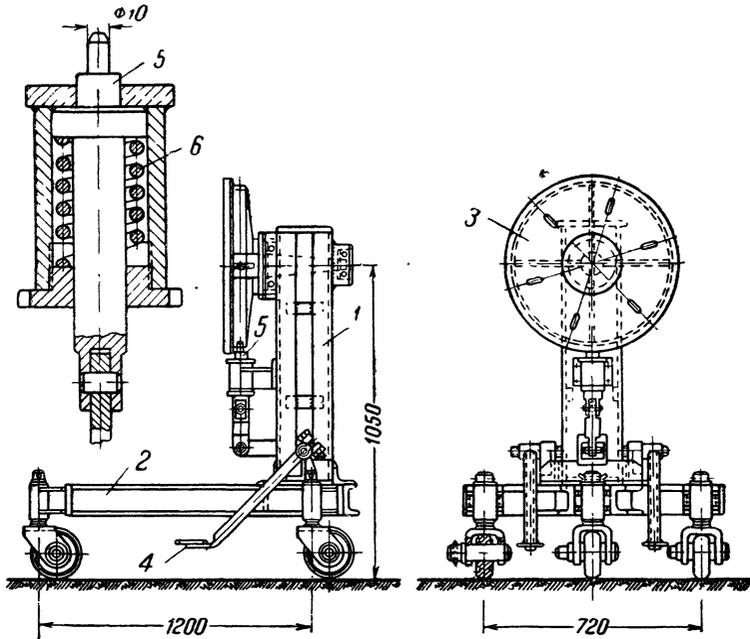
Подставка для сварки трубчатых изделий.
